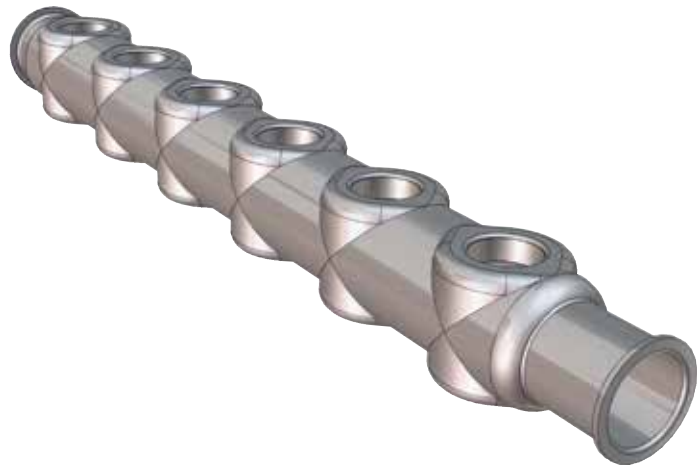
Collecteur en acier inox à plans parallèles alternés
